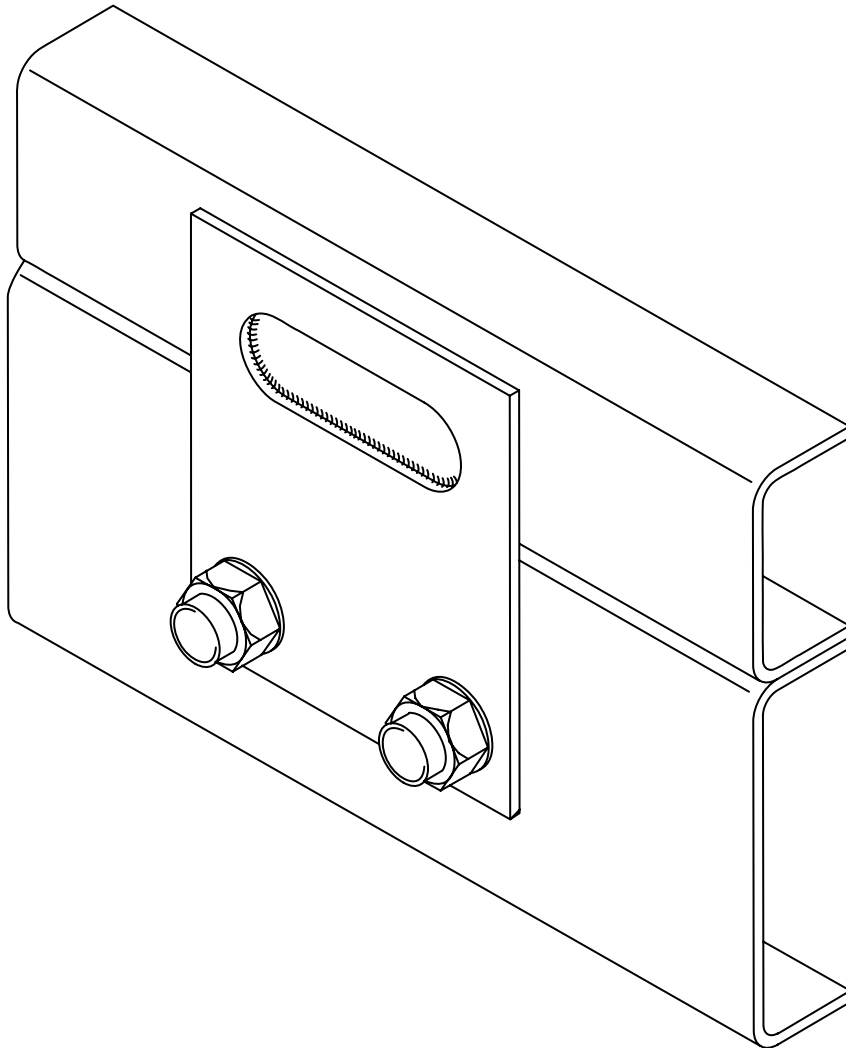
Hilfsrahmenbefestigung mit Lochschweißung ESC-025
